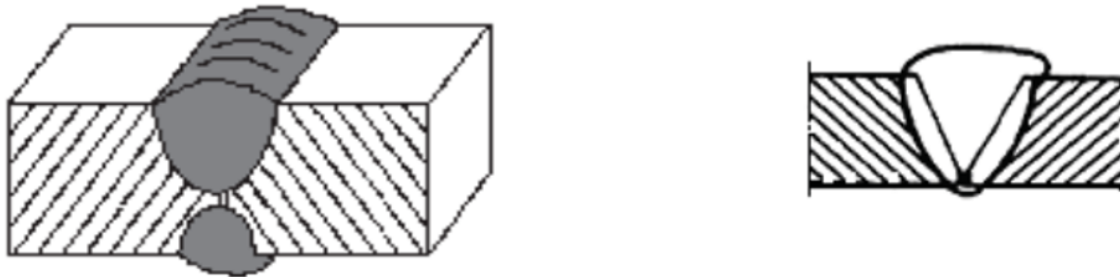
Эскиз дефекта сварного шва
